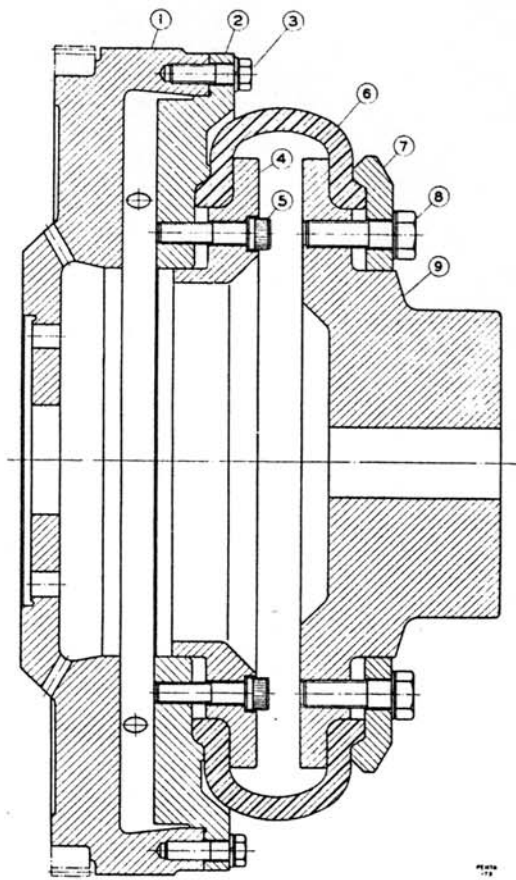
Elastisch Kupplung für das Schwungrad des Motors im Schnitt.
